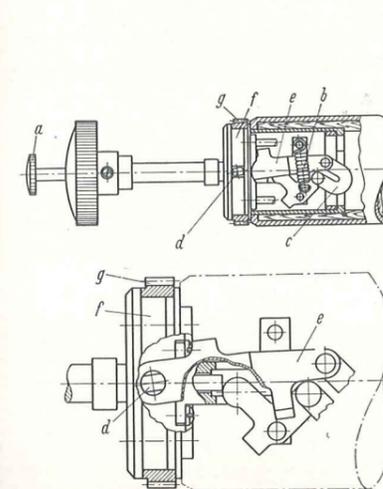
Spreizring – Klemmkupplung der Schreibmaschinen von VEB Büro-maschinenwerk Sömmerda
